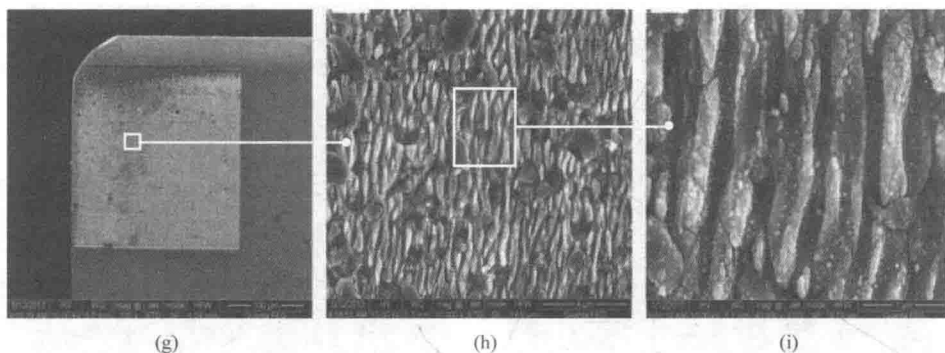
陶瓷刀具表面飞秒激光加工的微织构形貌
